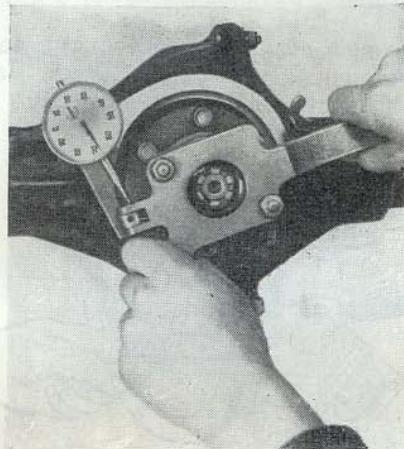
Проверка бокового зазора в зацеплении шестерен главной передачи
